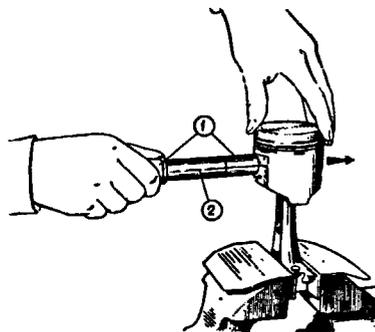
Запрессовка поршневого пальца в верхнюю головку шатуна: 1 - приспособление А60325; 2 - поршневой палец. Поршень должен опираться на головку шатуна в направлении, указанном стрелкой
